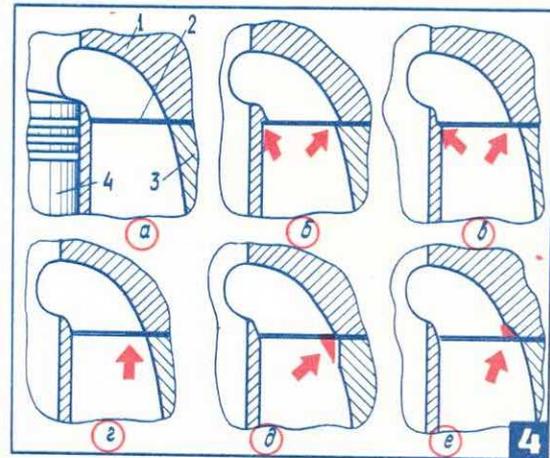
Взаимная подгонка сечений продувочного канала на стыке цилиндра и картера: а — нормальный канал; б, в — возможные дефекты изготовления; г — выступающая прокладка; д, е — неправильные способы подгонки сечений; 1 — цилиндр; 2 — прокладка; 3 — картер; 4 — поршень в положении НМТ.
